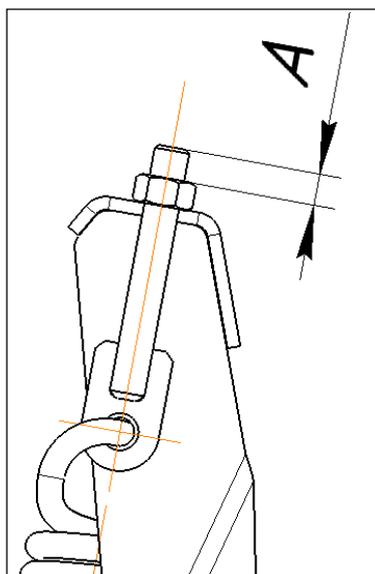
Размер «А» выхода резьбовой части натяжителя без предварительного натяжения пружин подвески
